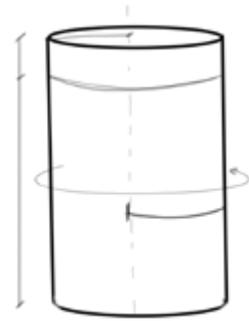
Dimensiones generales del packaging. Fuente: Propia
